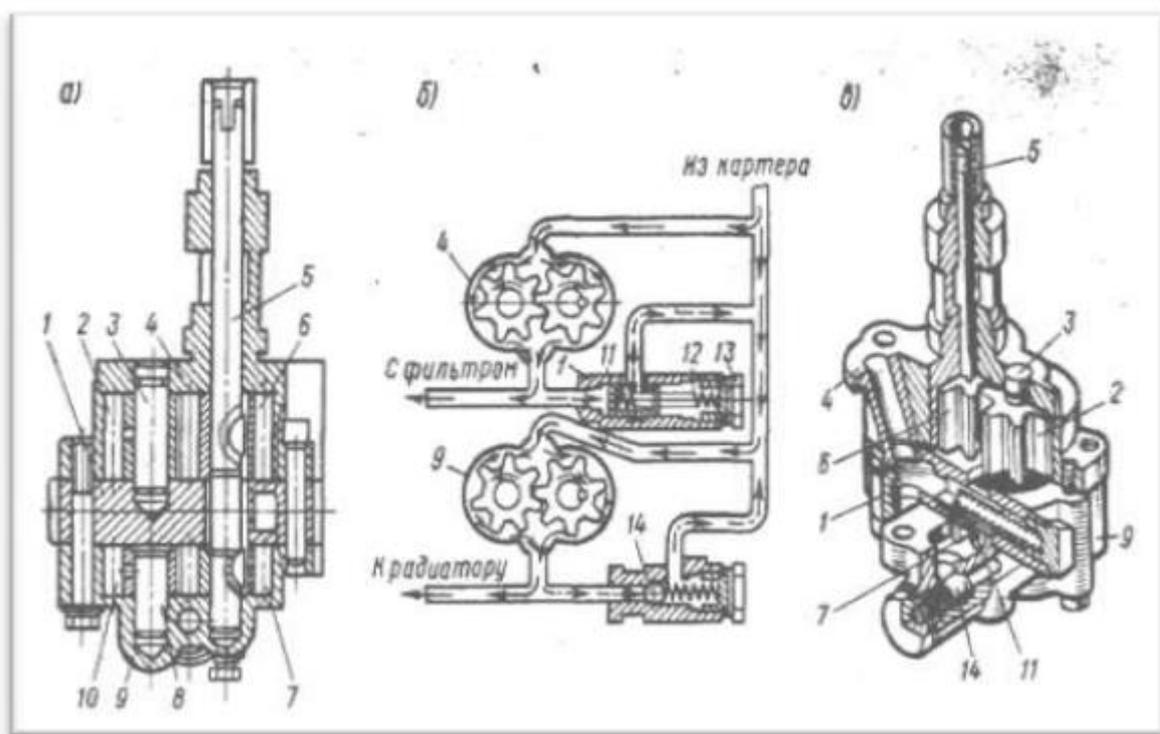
Устройство двухсекционного масляного насоса: а - продольный разрез; б - схема работы; в - общий вид
